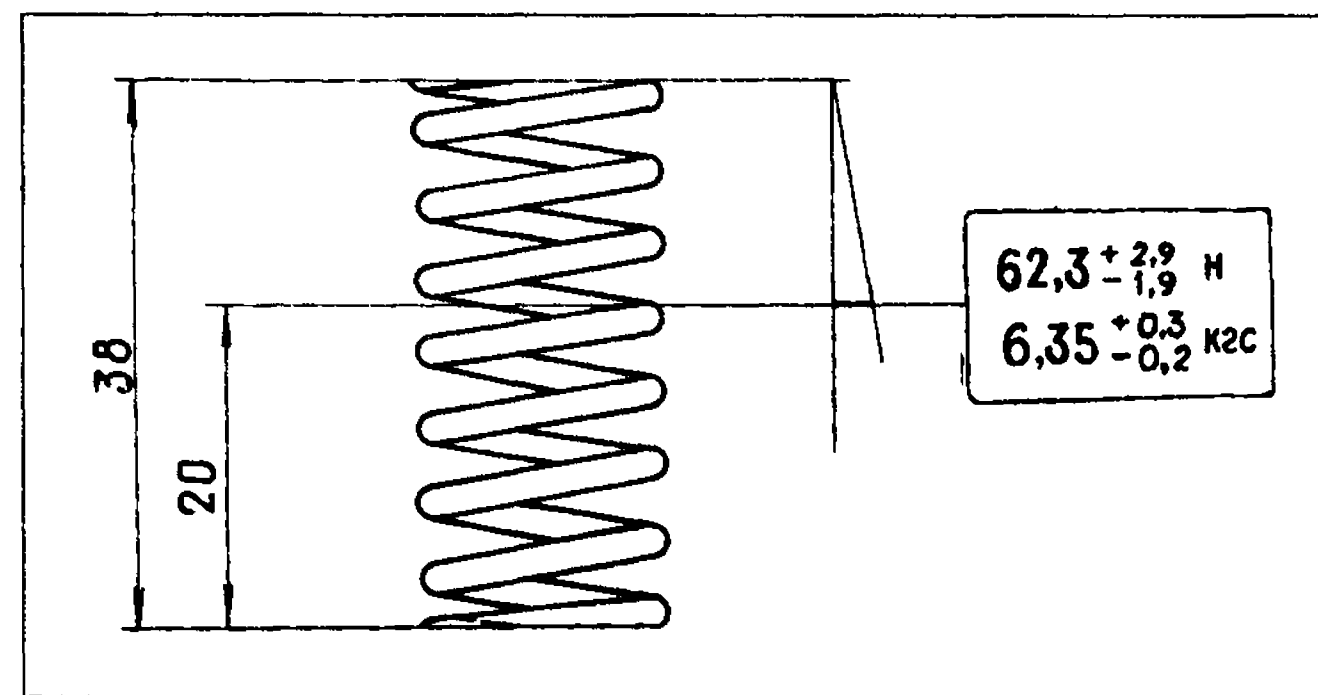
Основные данные для проверки пружины редукционного клапана
